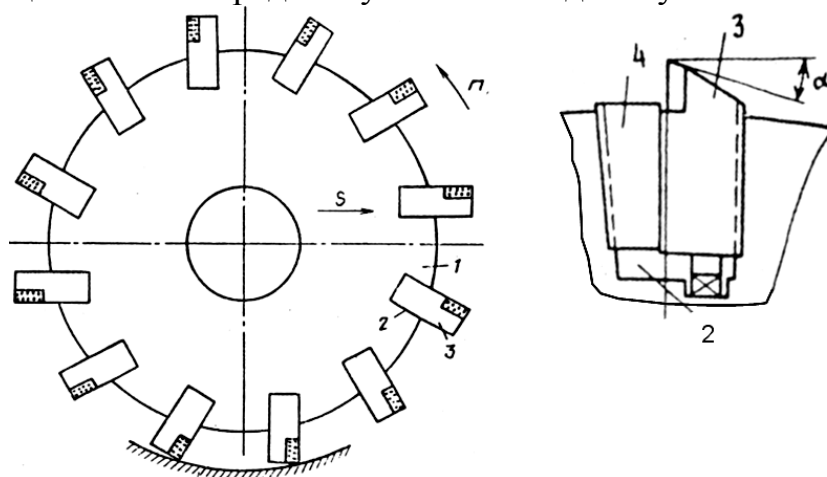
Дисковая фреза 1 со вставными ножами 3 с напайными пластинами из твердого сплава и их крепление в пазу 2 дополнительным клином 4 с рифлениями
